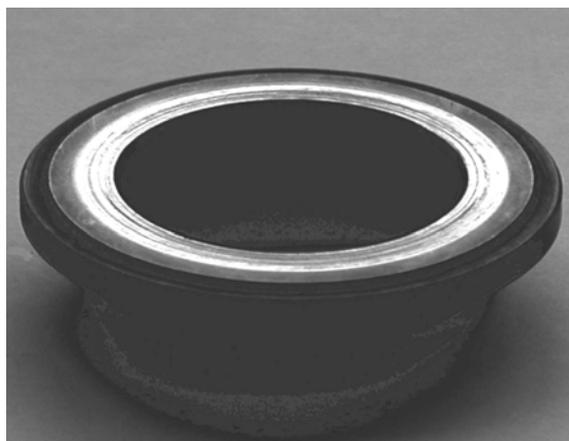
Поверхность трения кольца из стали 40X13, имеющего ступенчатый износ со следами схватывания.
